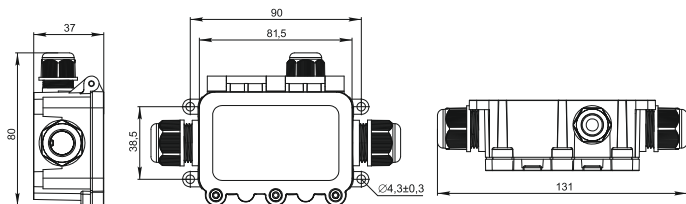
Габаритные размеры коробки WTP-407 / Figure 8 – Overall dimensions of the WTP-407 box
